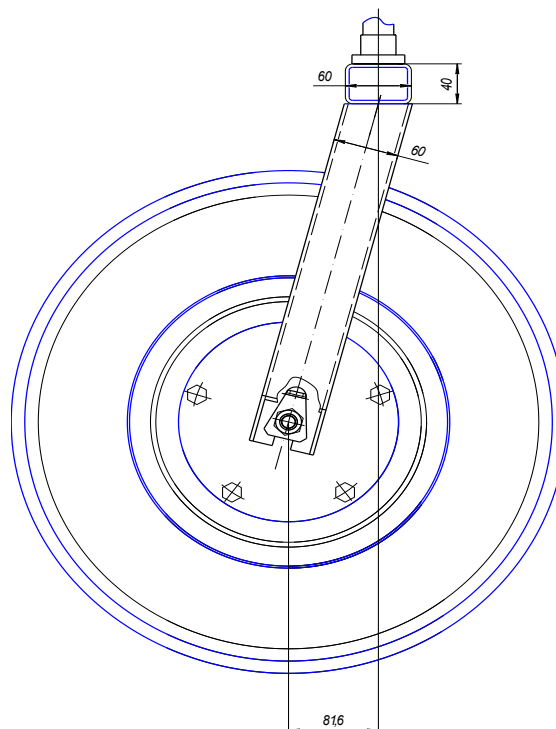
Конструкція вдосконаленої самокерованої передньої вилки
